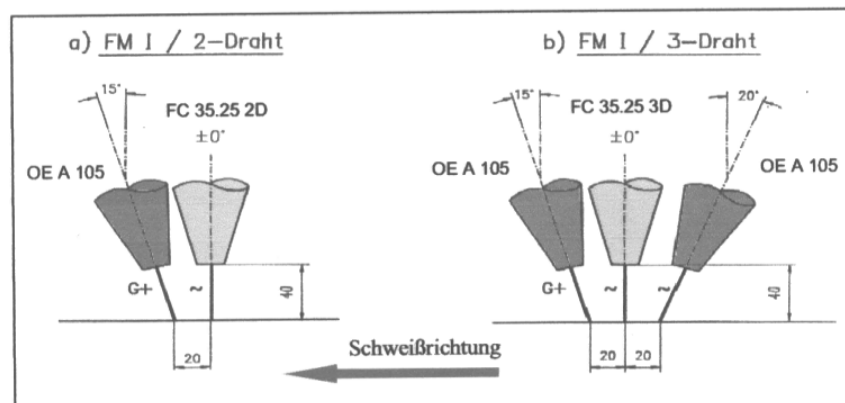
Anordnung der Drahtelektroden und Schweißkopfstellung beim UP-Mehrdrahtschweißen mit dem FMI-Prozeß
